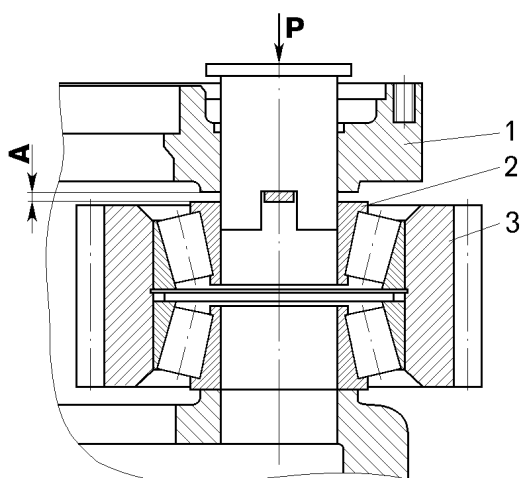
Регулировка подшипников сателлитов второго ряда:
